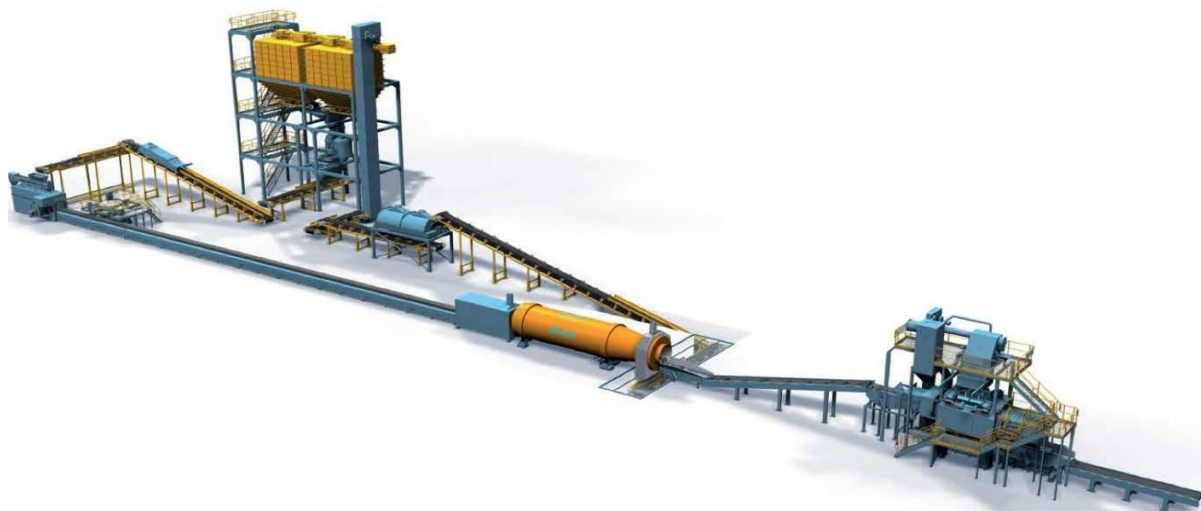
Общий вид АФЛ с комплексом оборудования для приготовления смеси и финишной обработки отливок
